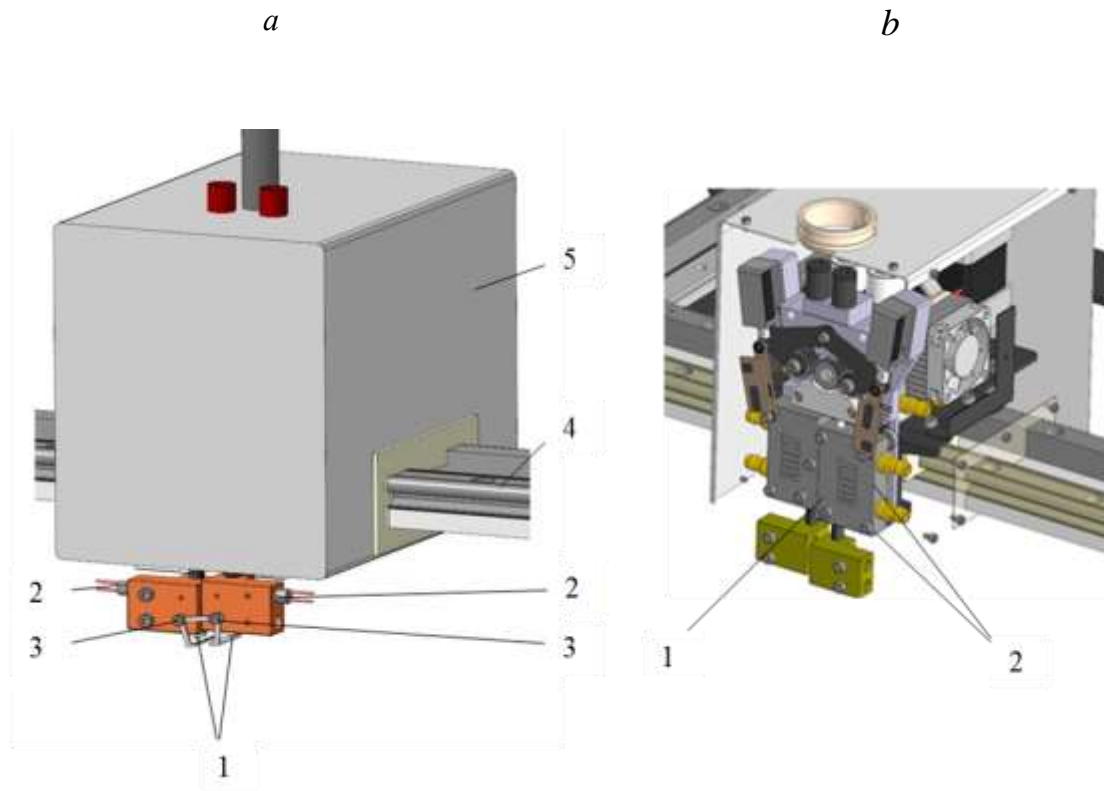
Экструзионный блок: *a* – вид в сборе: 1 – сопла, 2 – нагревательные элементы; 3 – клапан; 4 – рельсовая направляющая; 5 – термоизолирующий корпус;
